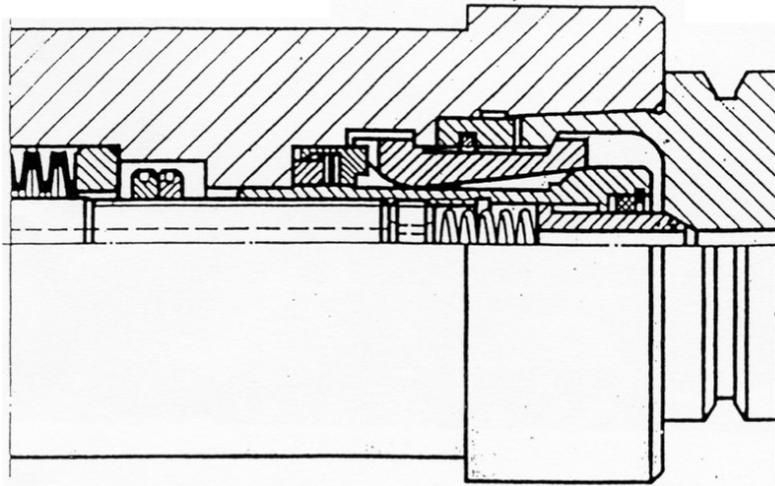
Spindel-Werkzeug-Schnittstellen bei Fräsmaschinen, Hohlschaftkegel für hohe Drehzahlen
